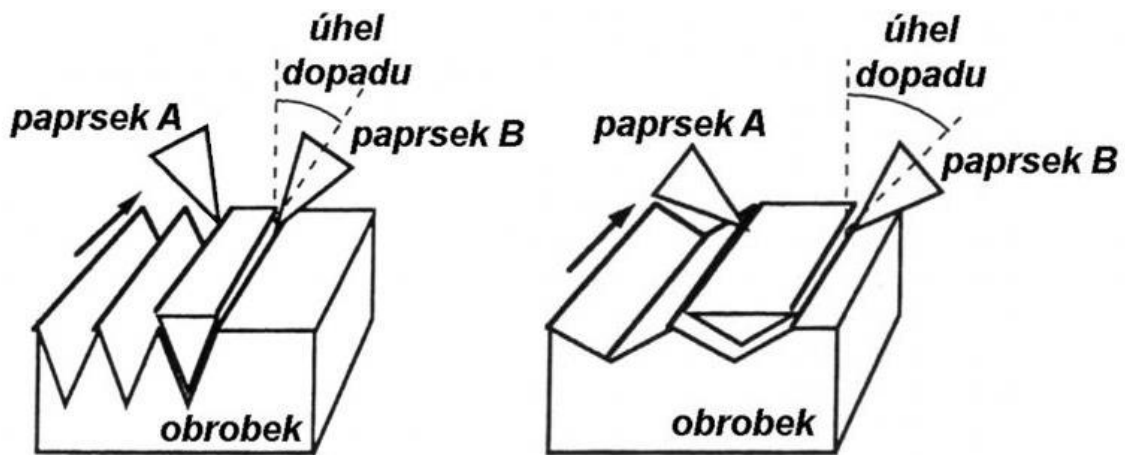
Princip šroubovicového (vlevo) a prstencového úběru materiálu [32]
